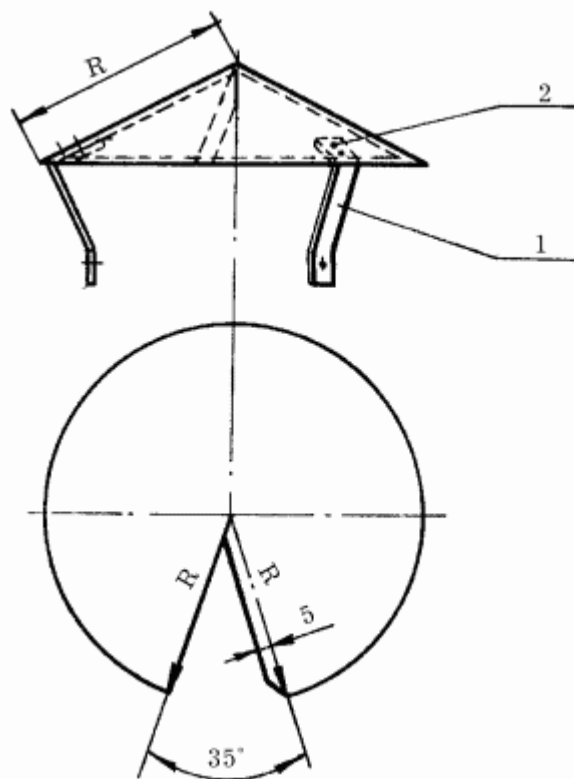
Заготовка для конического зонта: 1 – стойка; 2 – заклепка.
